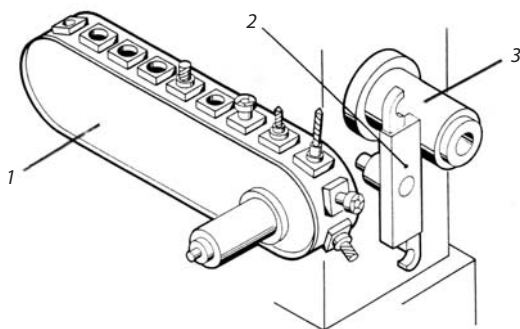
Схема смены инструмента из магазина автооператором:
